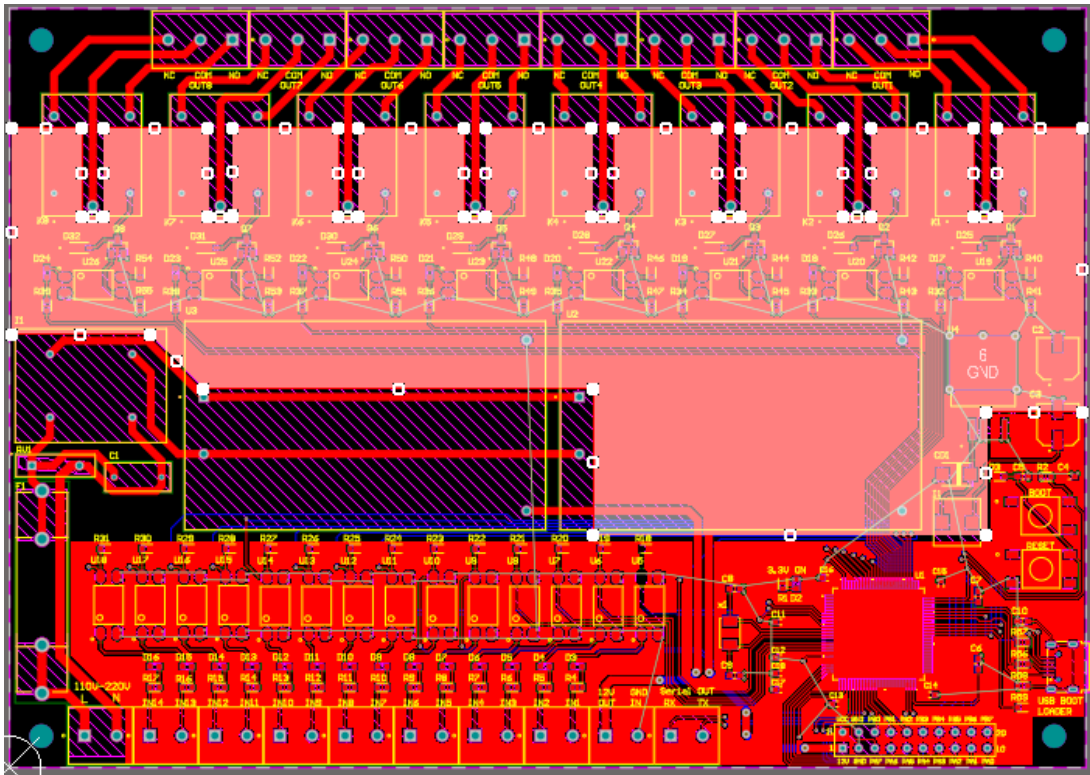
Ruteo de pistas de la capa superior e inferior del PCB.
